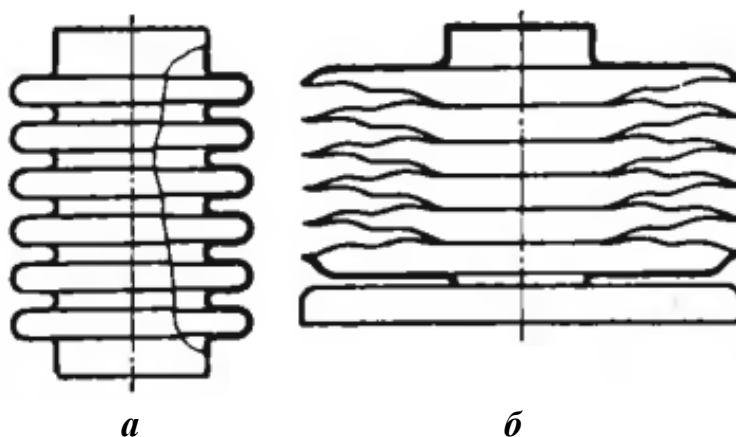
Сильфоны: а - бесшовный; б - сварной
